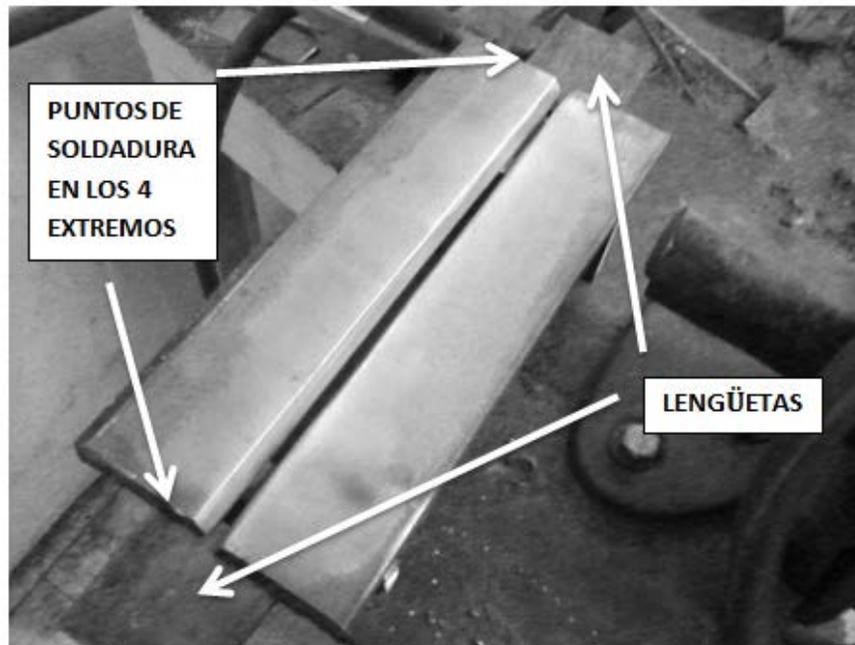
SOLDEO DE LAS LENGÜENTAS PARA LA PROBETA
